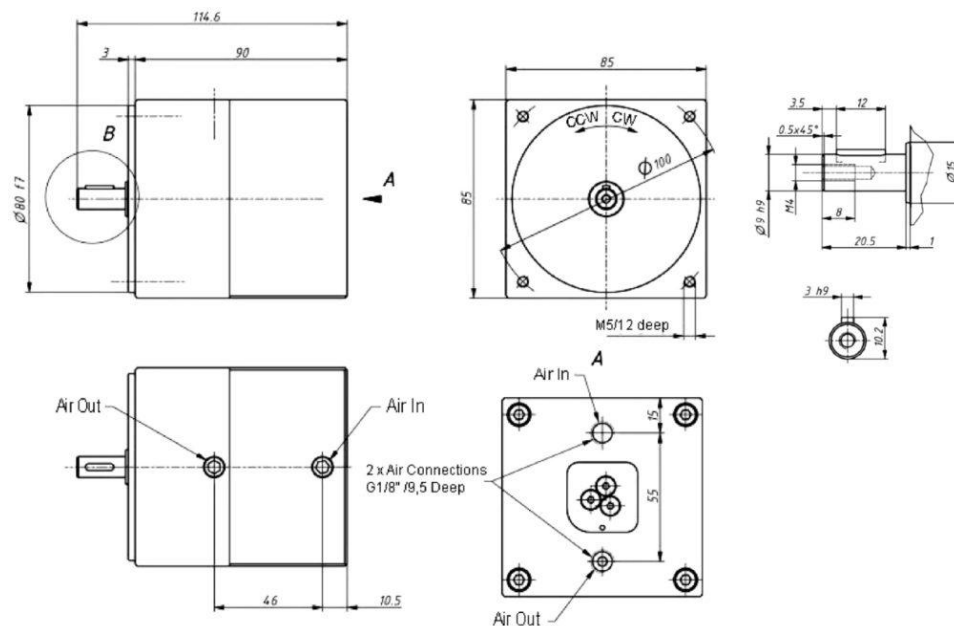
Конструктивні параметри пневмодвигуна RM004 GLOBE []
